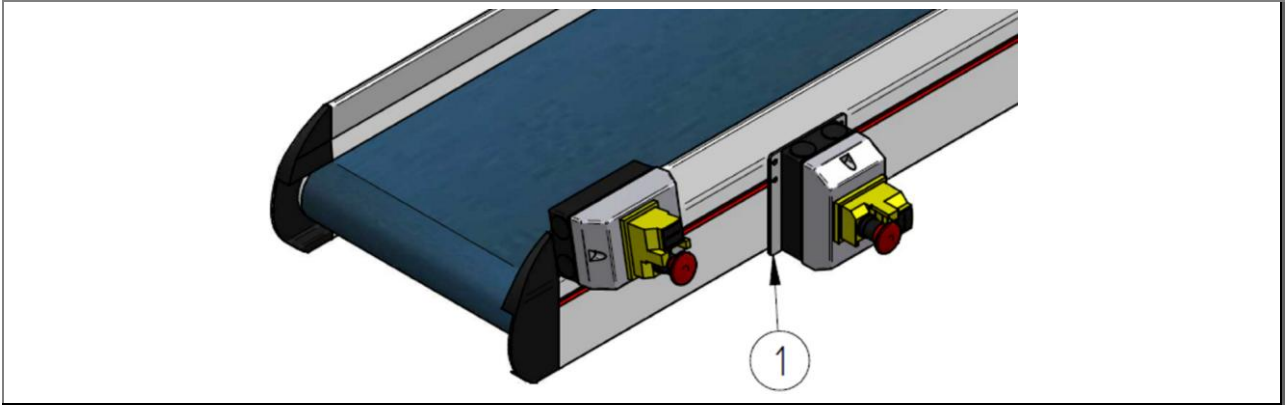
Soportes para interruptor principal - ZZ.982.0104.00
